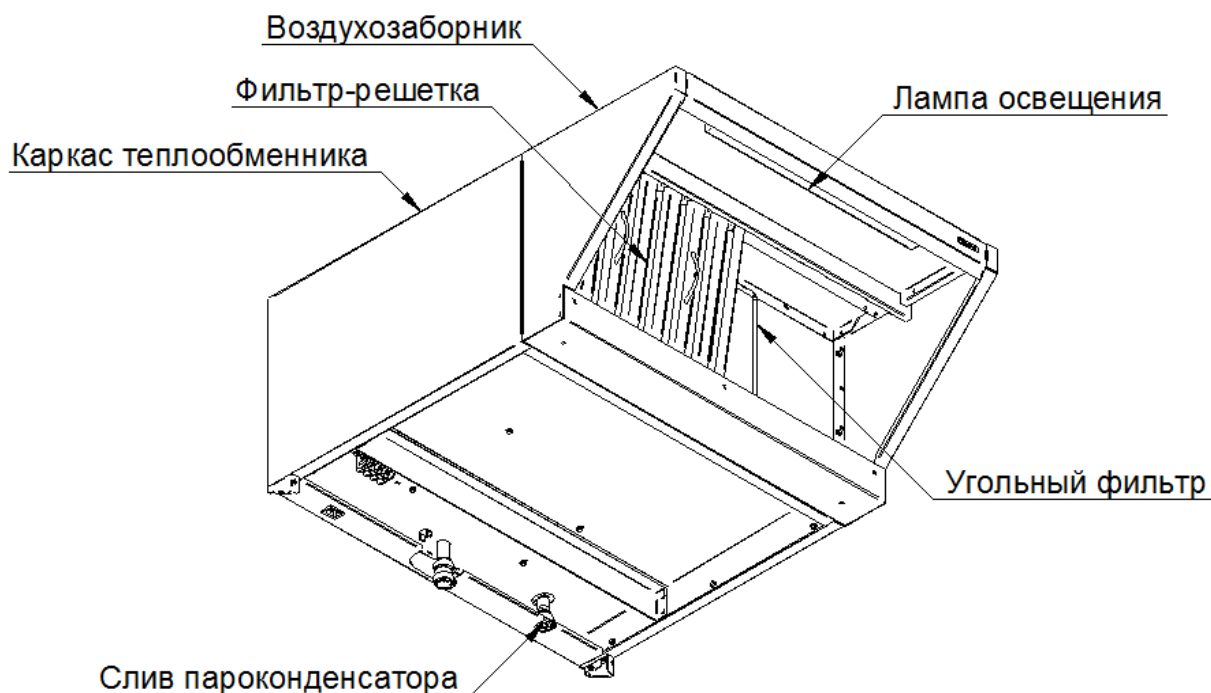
Внешний вид ЗВВ-4-6/4П
